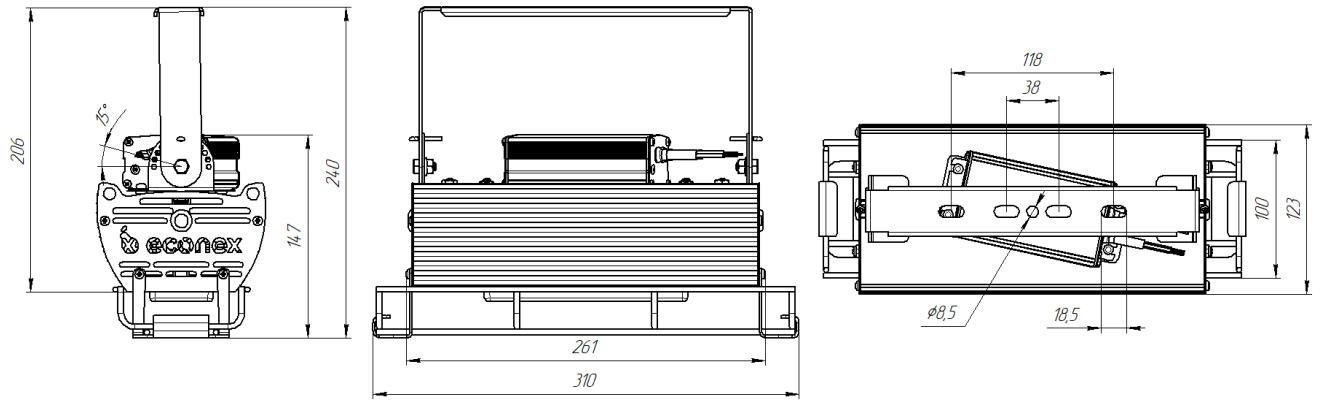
Габаритный чертеж светильника Ecolux Kvant 50 G3 ES
